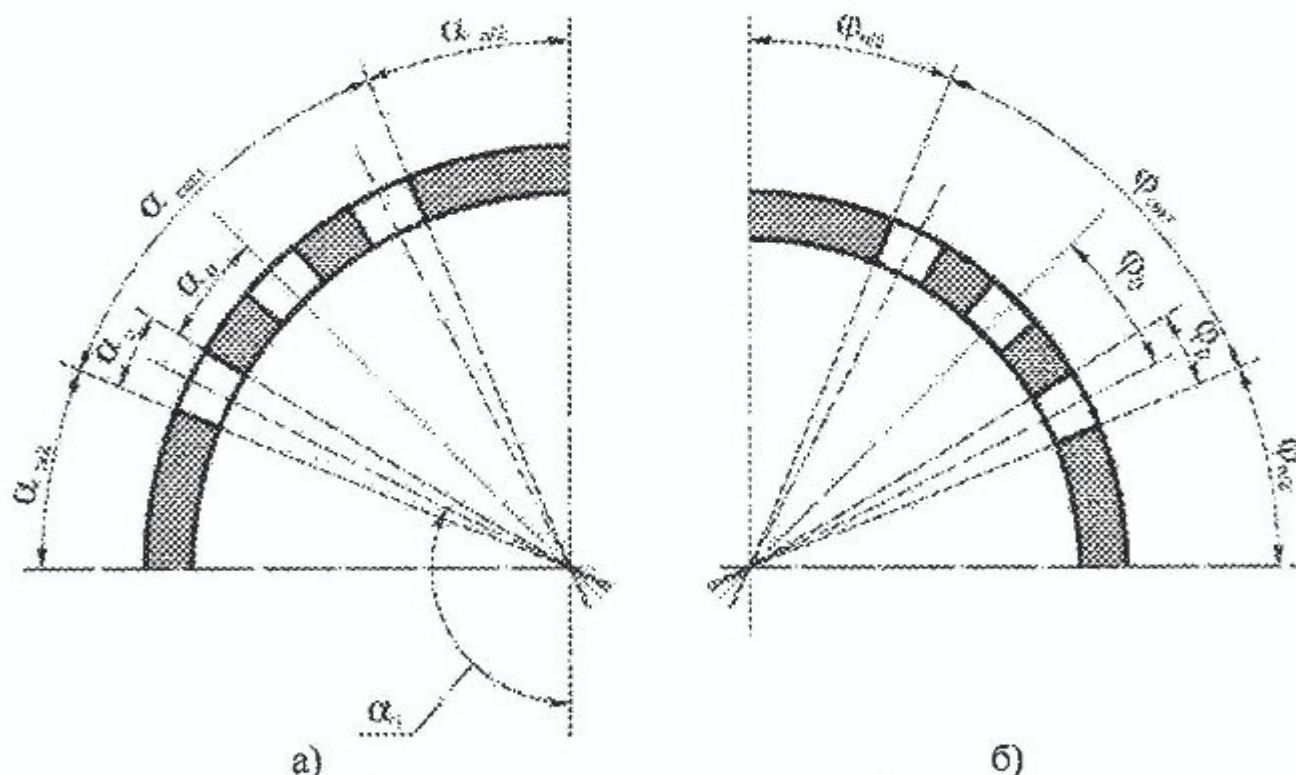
Угловые размеры решеток статора (а) и ротора (б)
